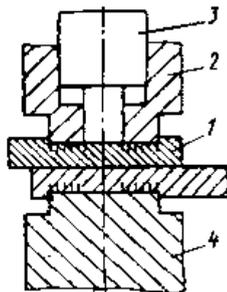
Схема точечной сварки с односторонним деформированием свариваемых деталей.
